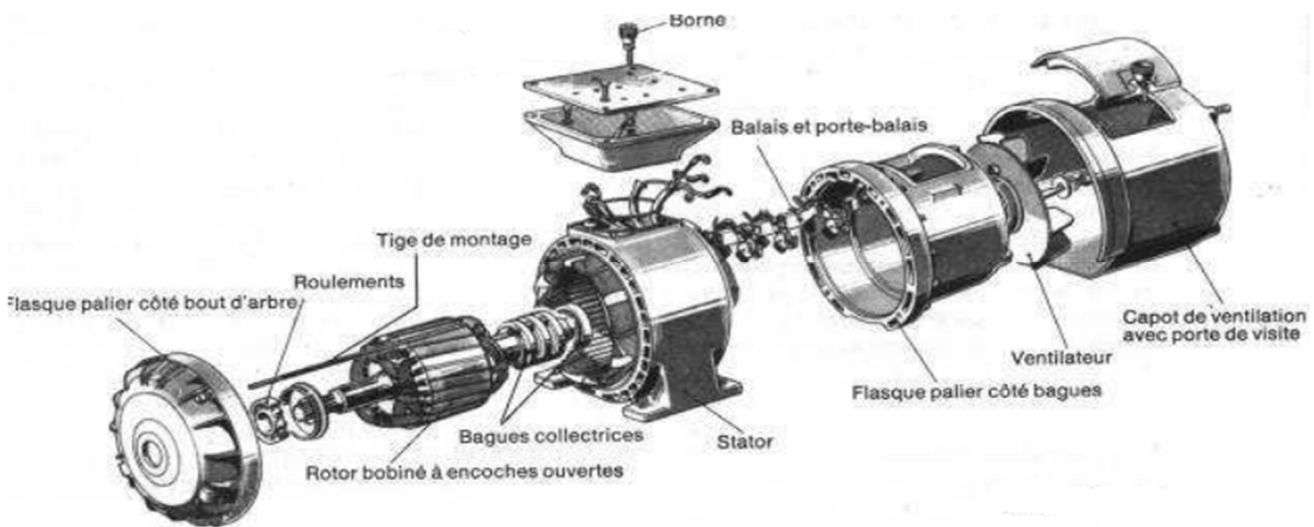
Moteurs à rotor bobiné ou moteurs à bagues. [6].
